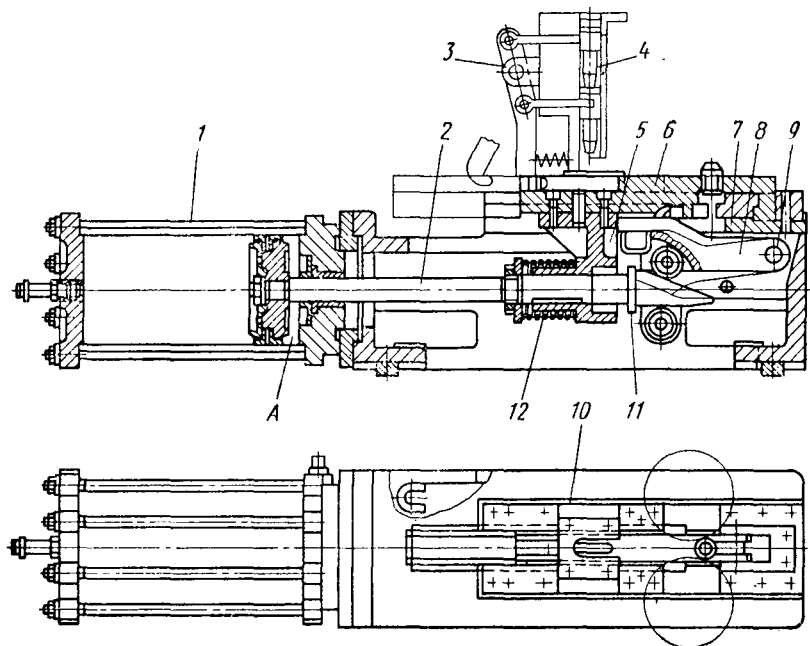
Автоматическое приспособление для фрезерования лысок
